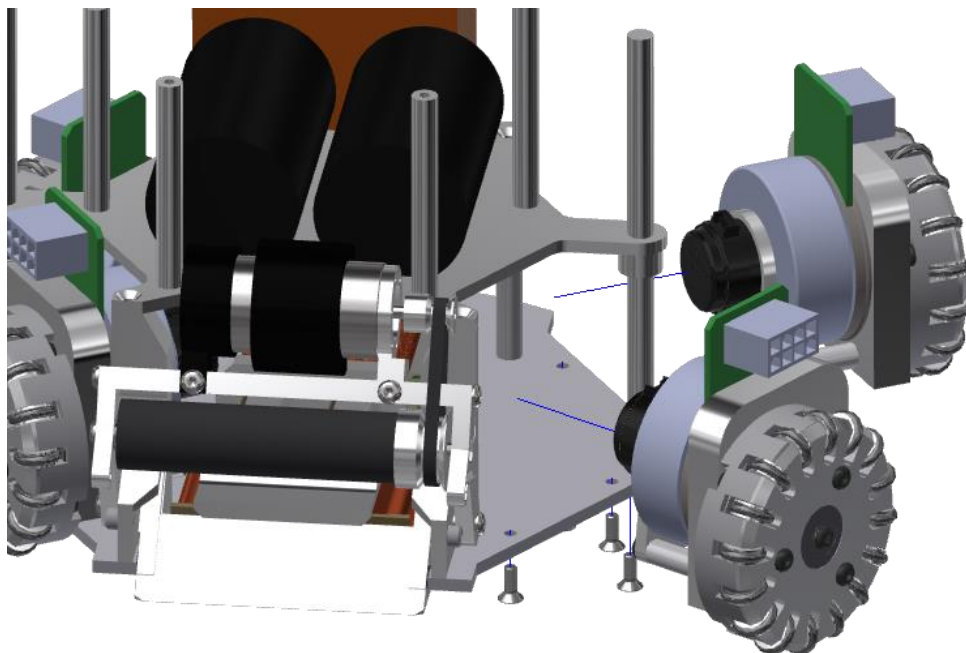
Conector na placa do motor a esquerda e fios soldados direto na placa do motor a esquerda
